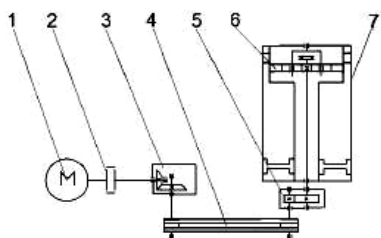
Кинематическая схема привода барабана самоходной фрезы:
